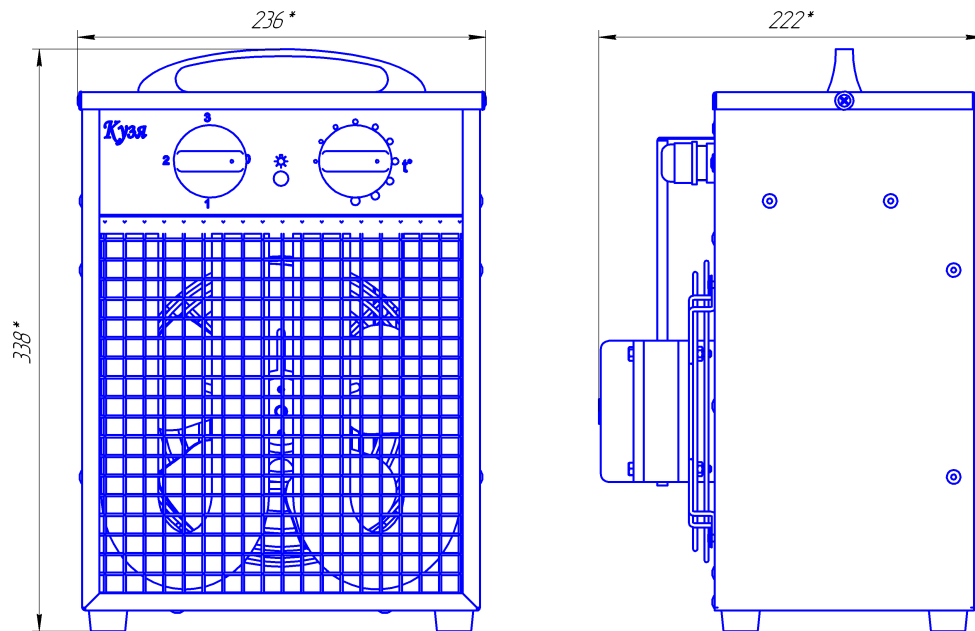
Калорифер КЗВ-3. Габаритный чертёж
